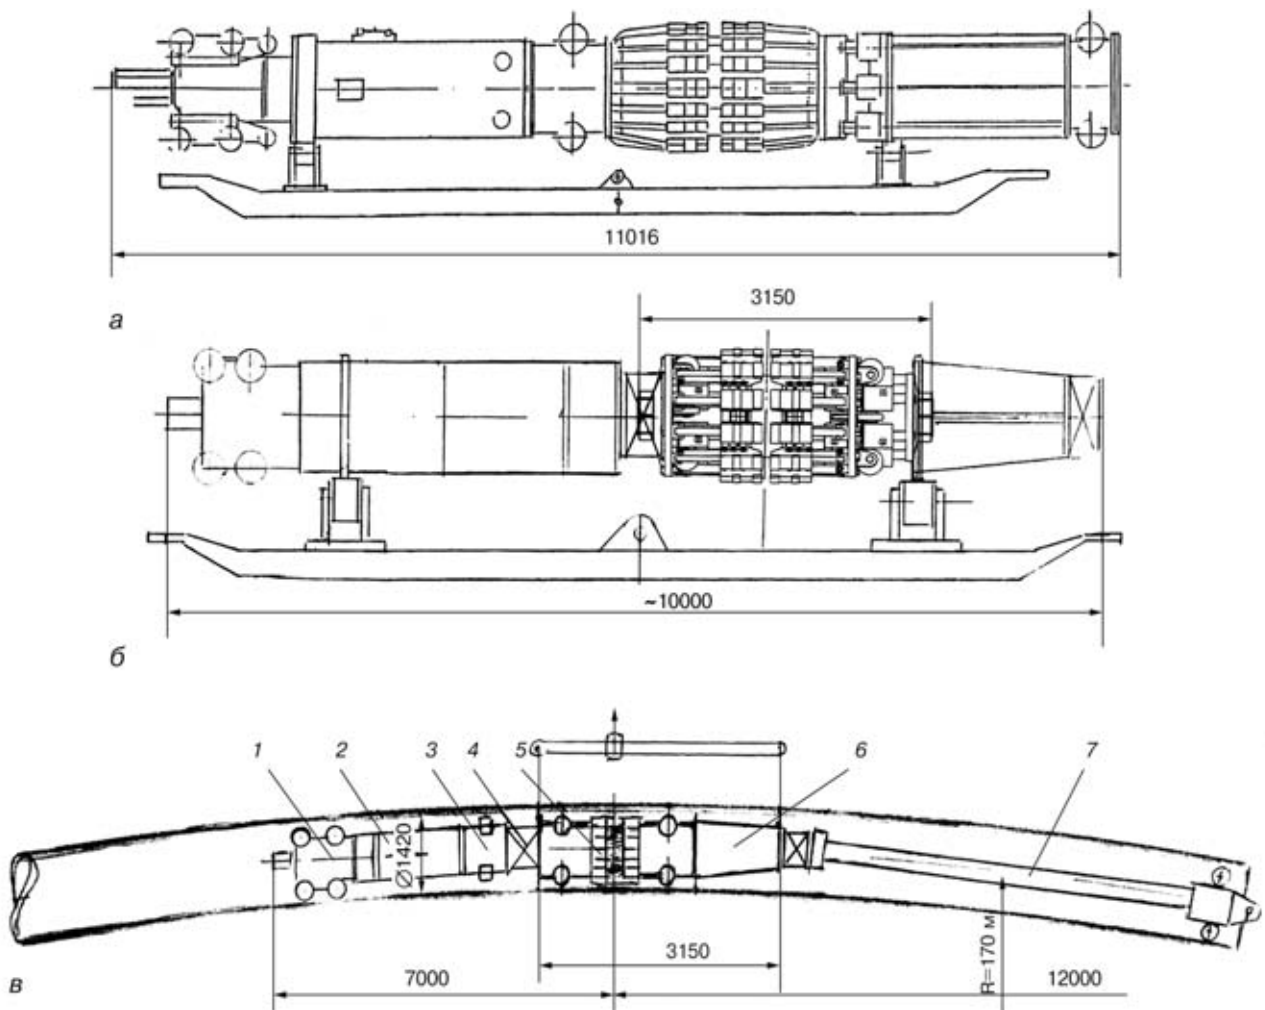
Схемы внутритрубных машин К 700 (а) и К 1007 (б) для контактной сварки труб диаметром 1420 мм; размещение машины К 1007 в трубе (в): 1 — привод перемещения; 2 — насосная станция; 3 — гратосниматель; 4 — шарнир; 5 — сварочная головка; 6 — гидротеск; 7 — штанга
